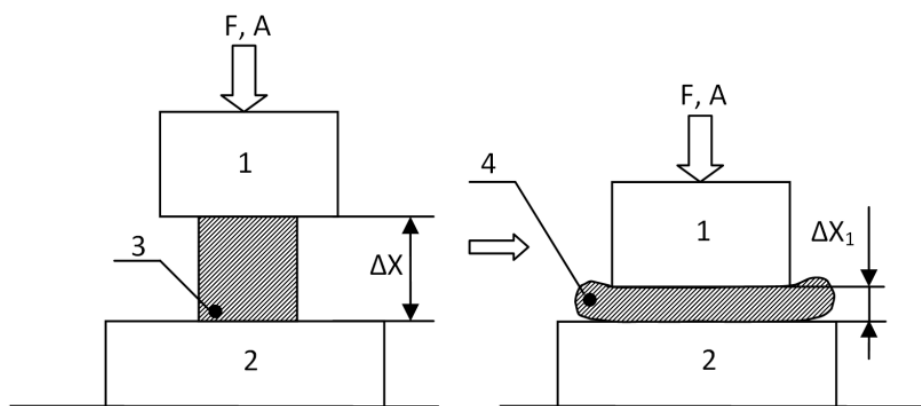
Схема воздействия УЗ колебаний на полимерный образец.
